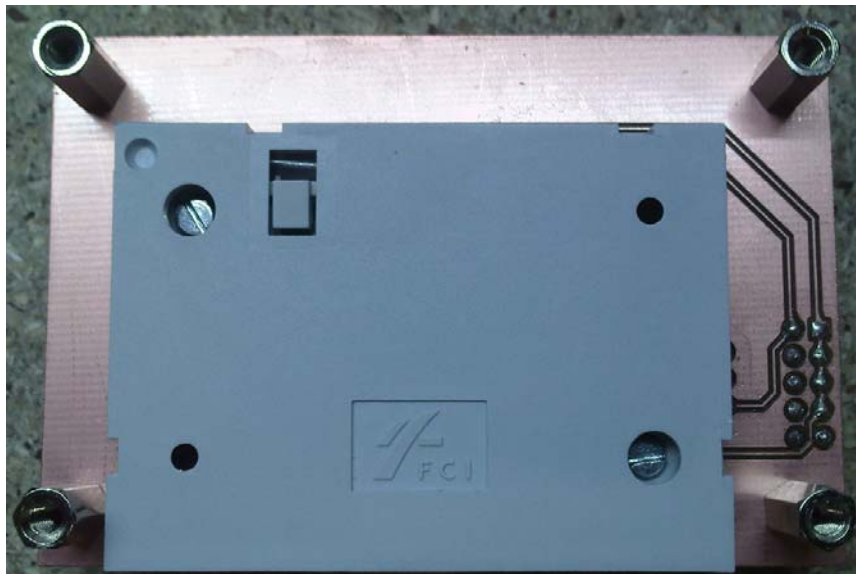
38: Fotografía de la cara inferior del PCB tras el montaje de componentes.
